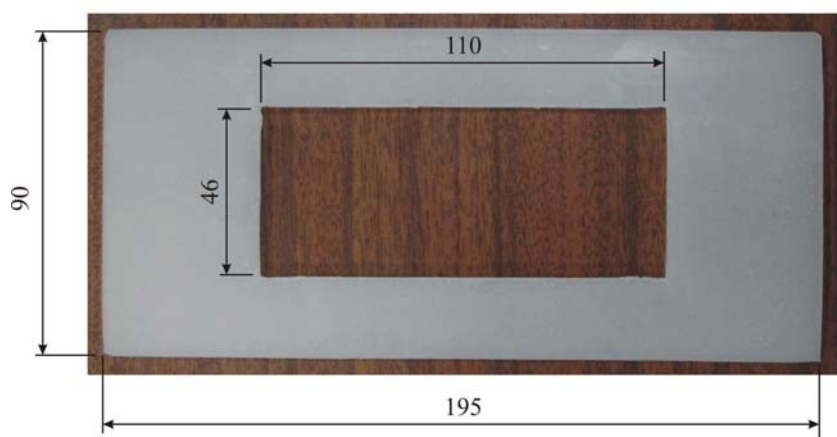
Quadro de silicone para fabricar placas de adesivo (dimensões em mm).
